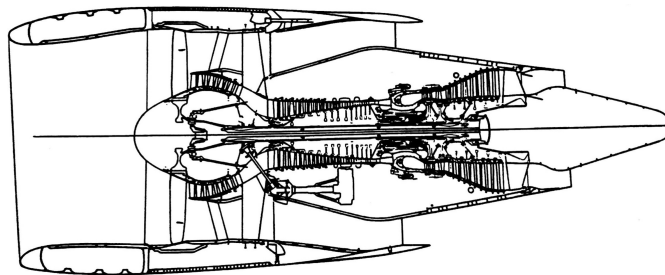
Modulová konstrukce motoru ADOUR / F405 [1]
